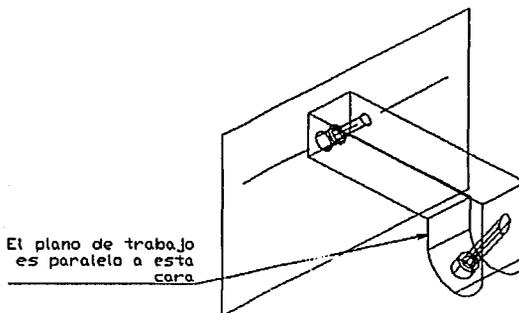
Plano de trabajo restringido por un eje y paralelo a un plano (On Edge/Axis & Planar Parallel).
